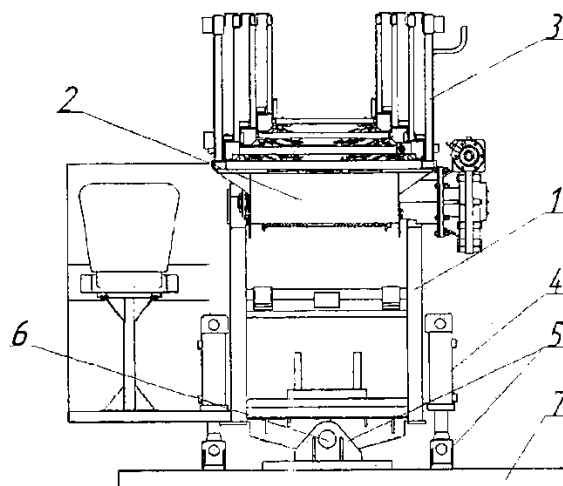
Схема бокового выравнивания пакета колен АЛ-30(43206)ЗСМИ:
